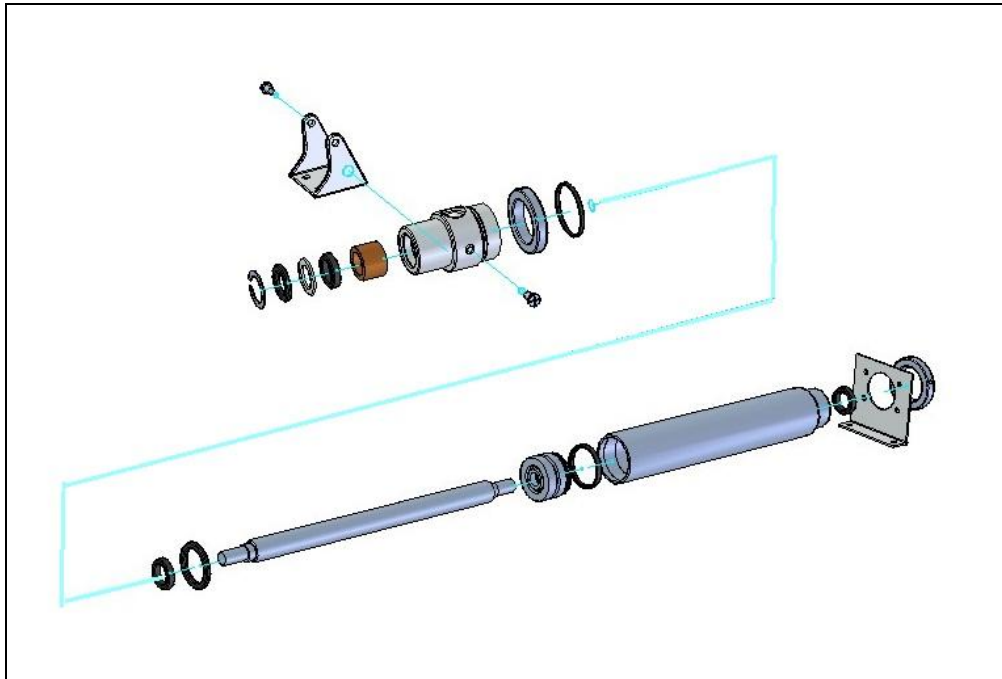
15 - Modelo de Cilindro de doble efecto - Explosionado
